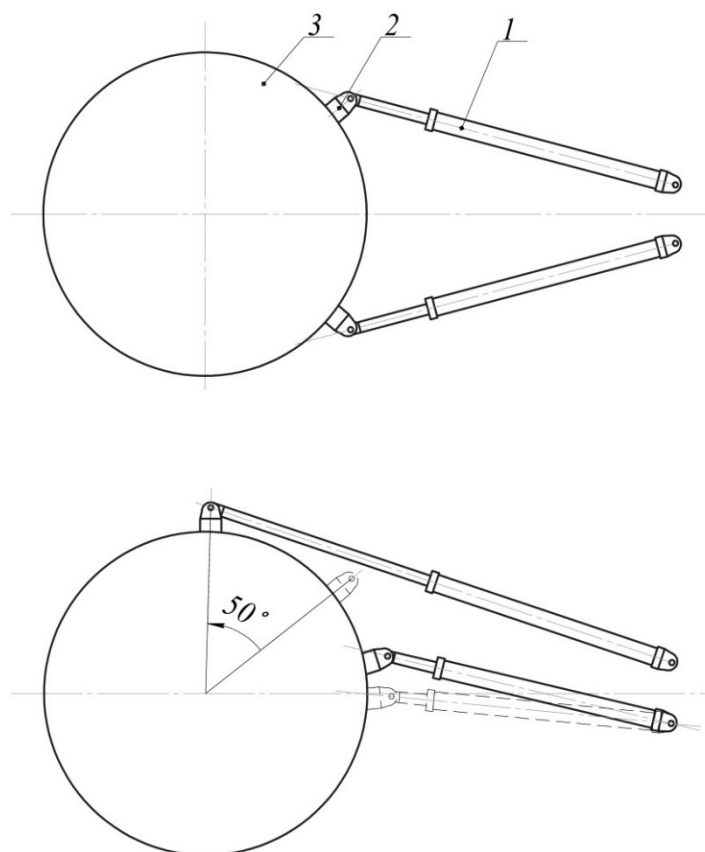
Схема опорно-поворотного устройства с 2 гидроцилиндрами:
